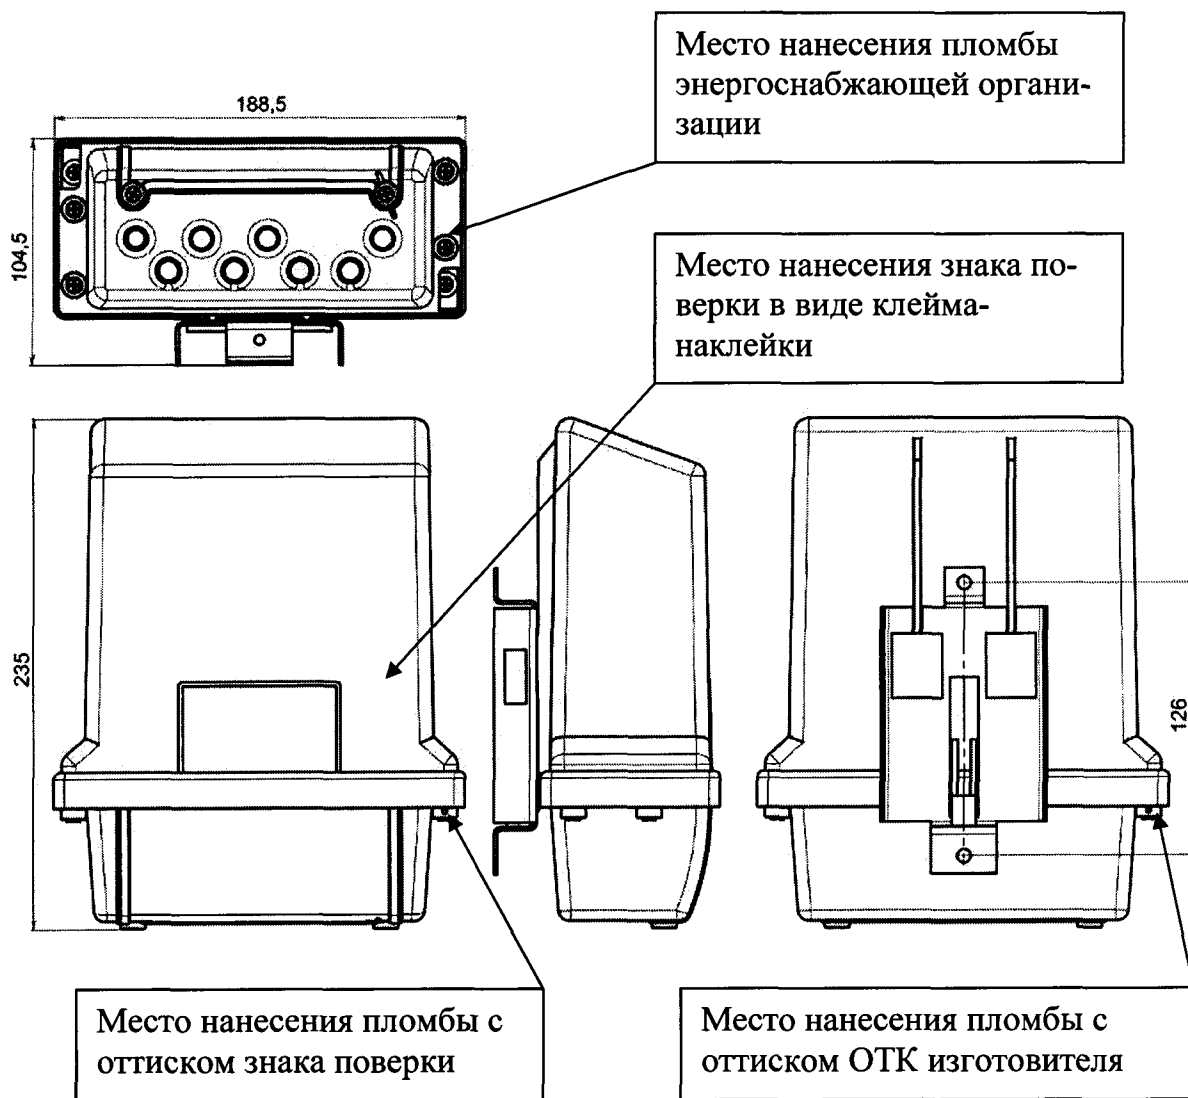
Места установки пломб и нанесения знаков поверки
